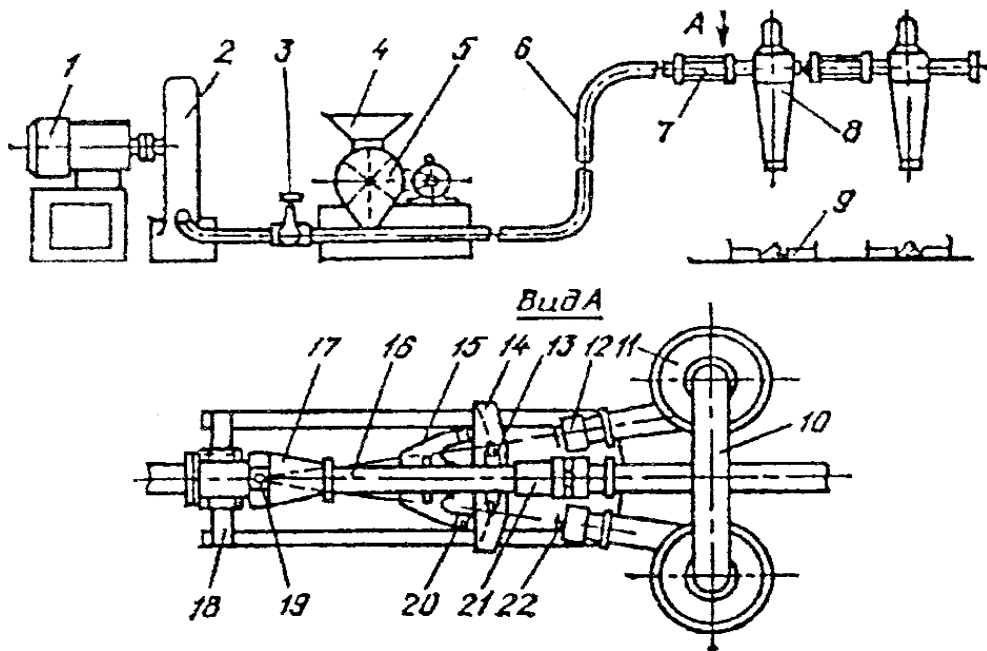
Конструктивна схема пневматичного транспортера ТПК-15:
